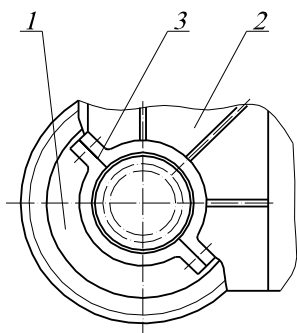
Конструкции ходовой части механизма передвижения крана: 1 – ходовое колесо; 2 – концевая балка; 3 – крепление ходового колеса к концевой балки
